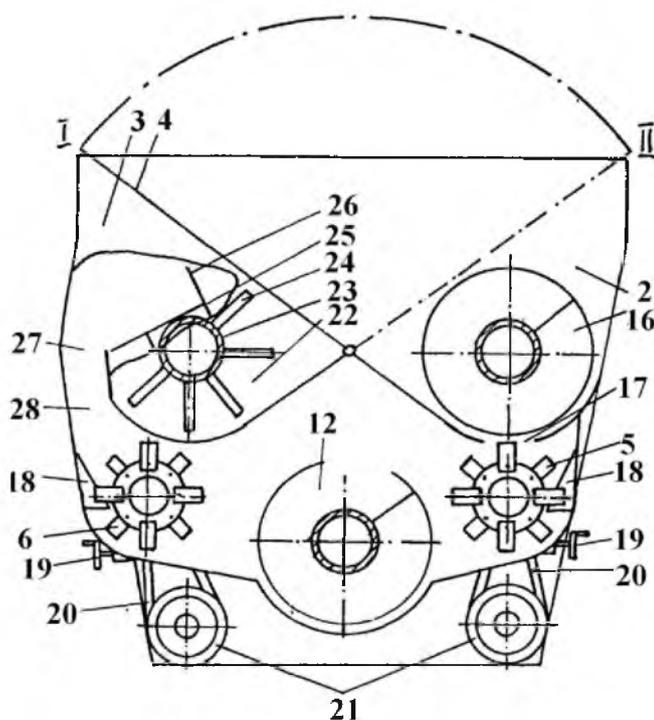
Мобильный кормоприготовительный агрегат (разрез А-А на рис.2):
